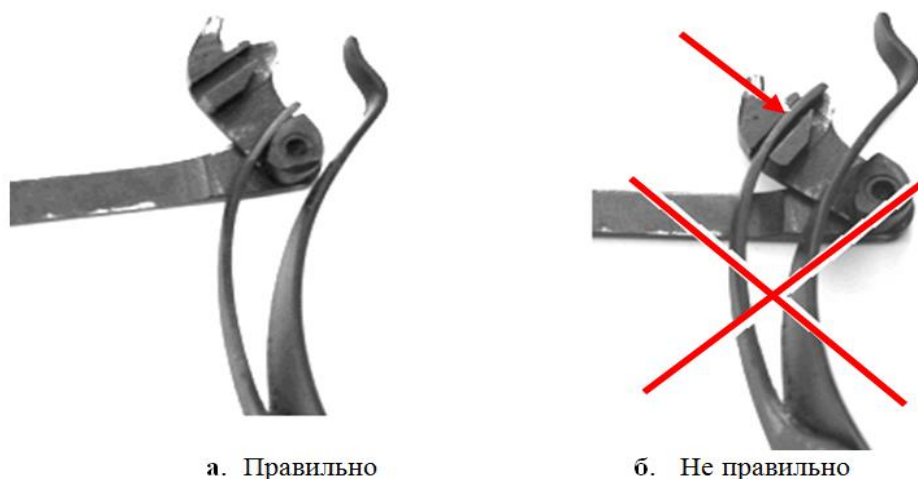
Положение узкого пера боевой пружины – на пяточке рычага взвода
